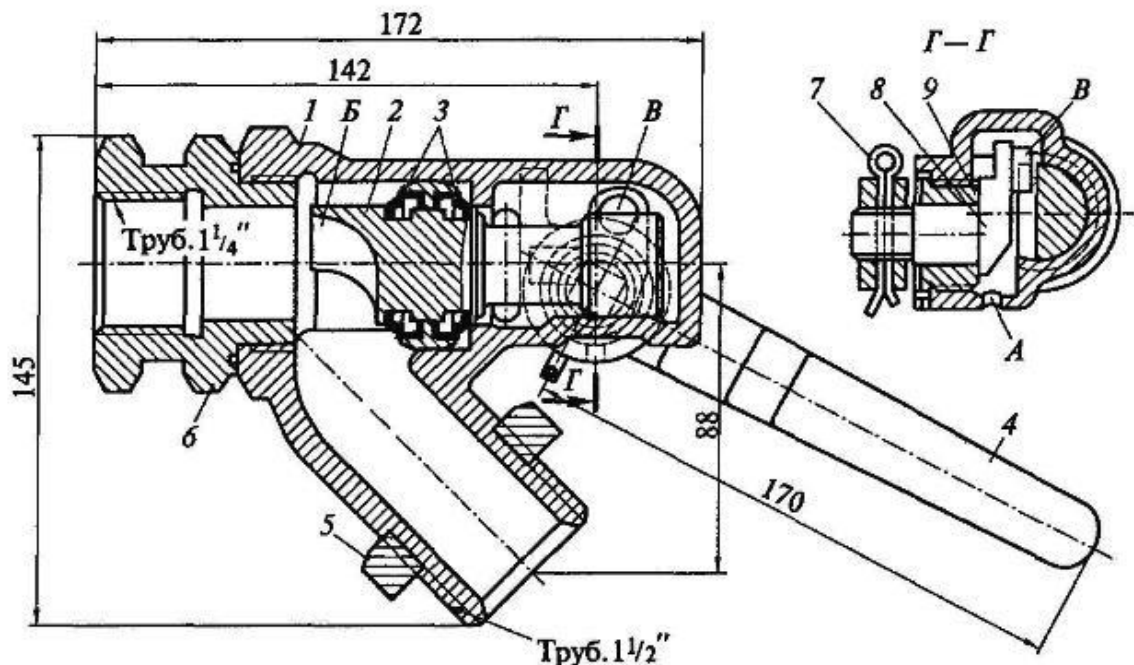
Кран повітряний КП 401–06.000 СК: 1 – корпус; 2 – клапан з відбивачем (напівсферичної поверхнею) Б; 3 – два гумових ущільнювальних кільця; 4 – ручка; 5 – контргайка; 6 – штуцер; 7 – шплінт; 8 – кулачок; 9 – гайка
